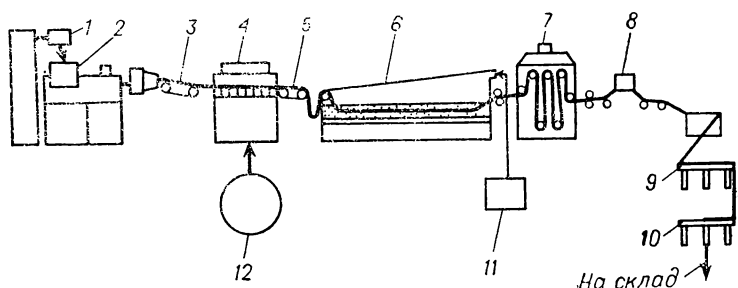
Схема линии вулканизации в псевдоожоженном слое: 1 — питатель; 2 — шприц-машина; 3 — приемный транспортер; 4 — машина для опудривания; 5 — отборочный транспортер; 6 — вулканизатор; 7 — устройство для охлаждения; 8 — станок для резки; 9 — контроль; 10 — комплектовка; 11 — газодувка; 12 — склад вспомогательных материалов.
